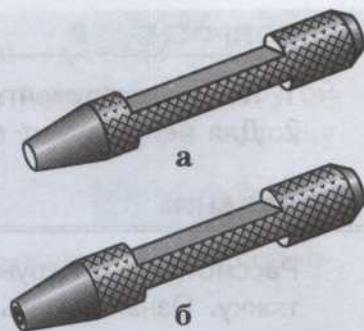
Поддержки для заклёпок с потайной (а) и полукруглой (б) головками
